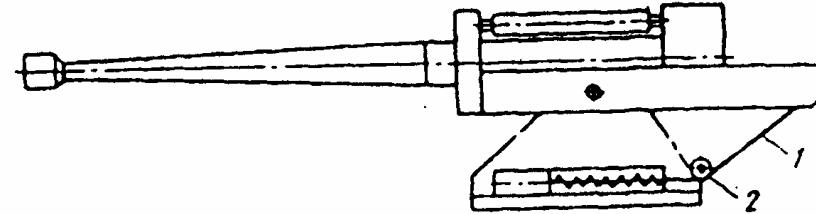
Схема уравновешивающего механизма тянувшего типа с неподвижной колонкой
